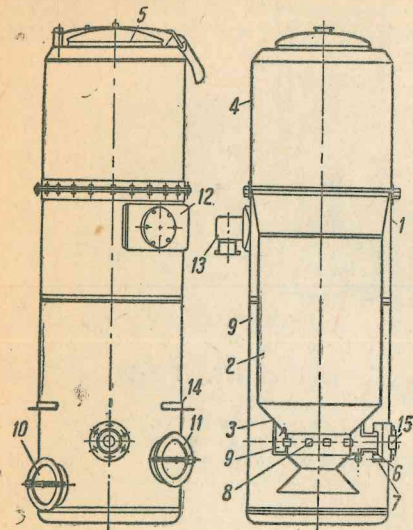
Газогенератор НАТИ Г-14: 1—наружный кожух; 2—бункер; 3—топливник; 4—верхняя часть газогенератора; 5—загрузочный люк; 6—соединительная гайка; 7—камера гайки футорки; 8—фурма; 9—воздушная камера; 10—люк для очистки зольника; 11—люк для закладки угля; 12—газоотборное полукольцо; 13—газоотборный патрубок; 14—опорный кронштейн; 15—шарнирная заслонка
